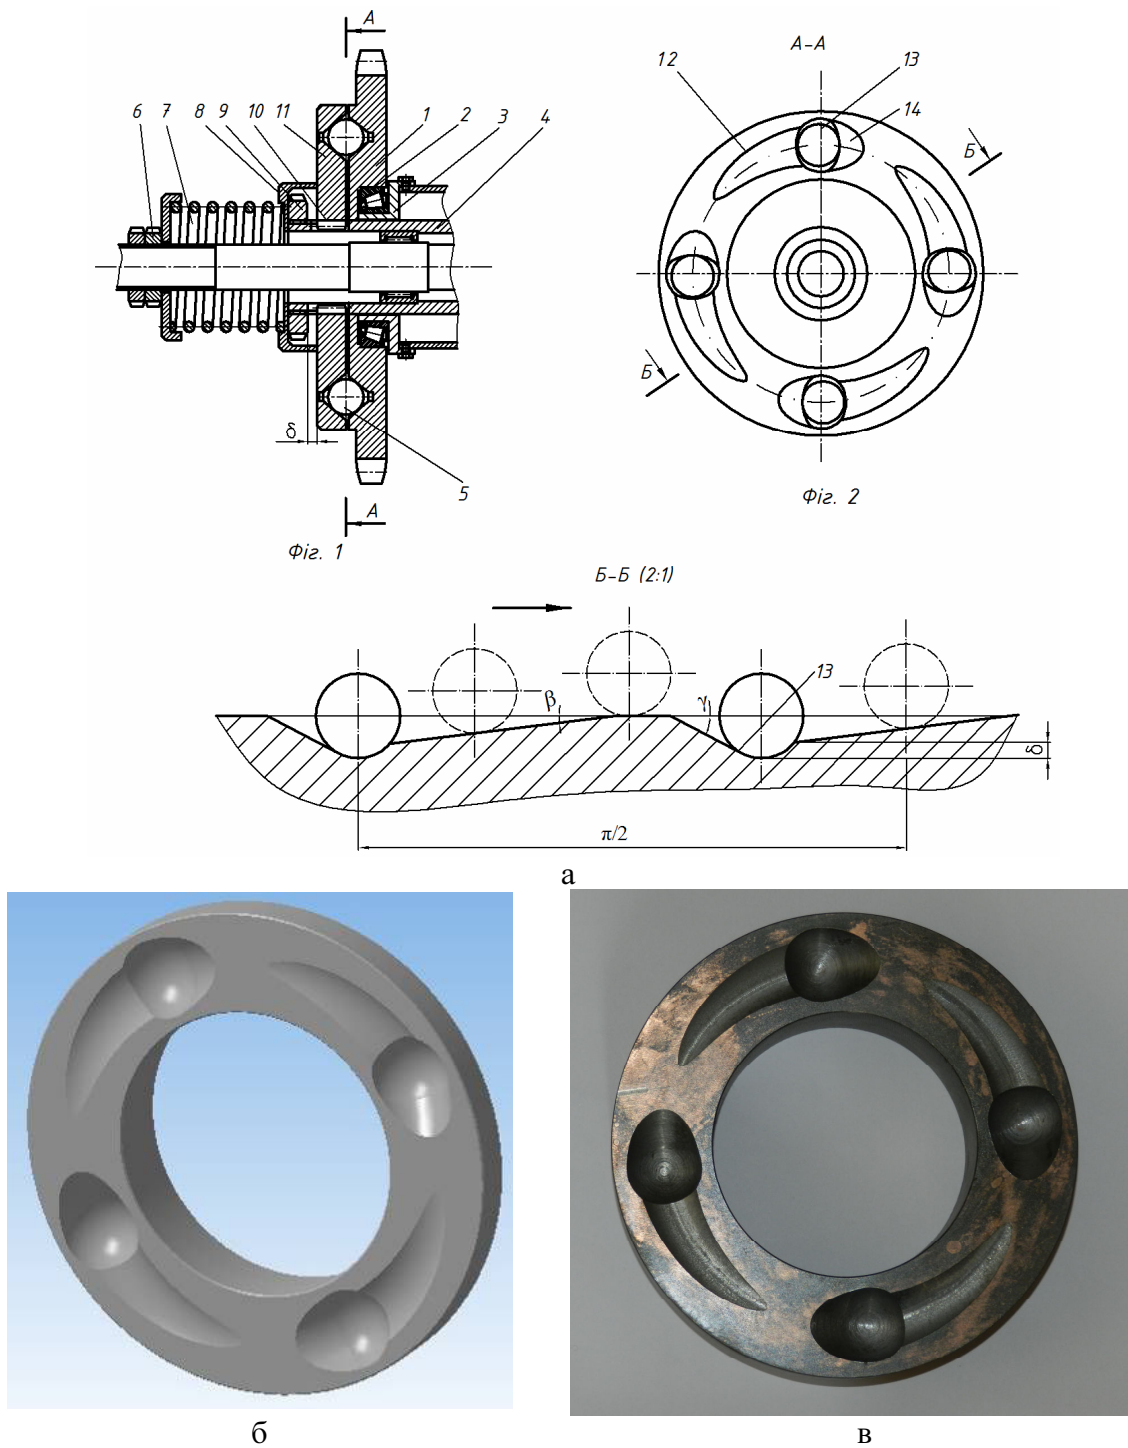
Конструктивна схема запобіжного пристрою (а) та загальний вигляд робочої поверхні ведучої півмуфти; б – модель, виконана в КОМПАС 3D; в – загальний вигляд виготовленої пів муфти
